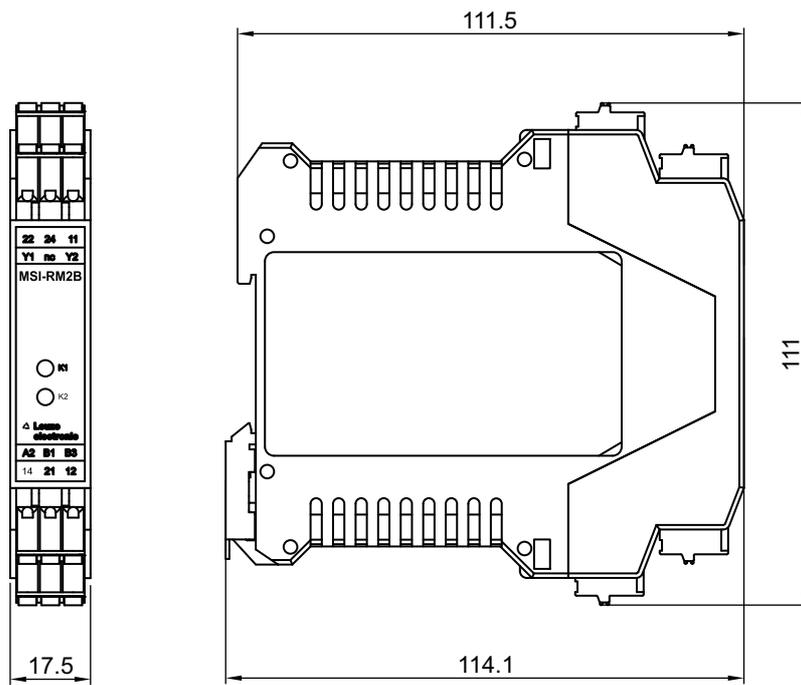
Dimensioni dell'MSI-RM2B-02
